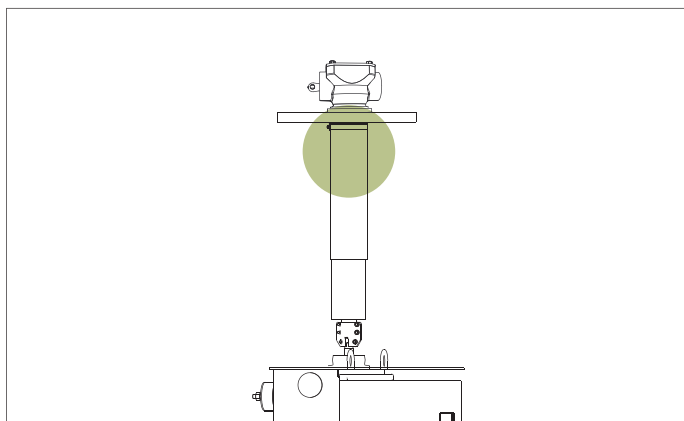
Установка защитного патрубка, больший диаметр вверх
